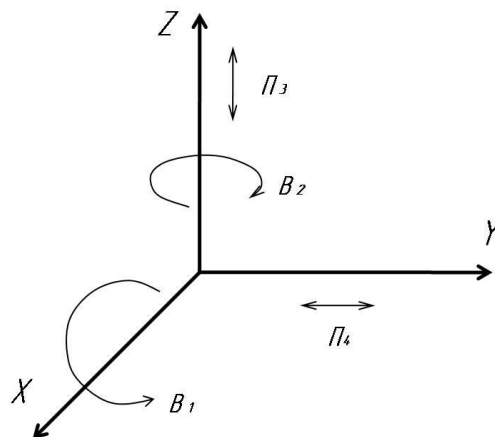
Ориентация движений исполнительных органов универсального фрезерного станка
